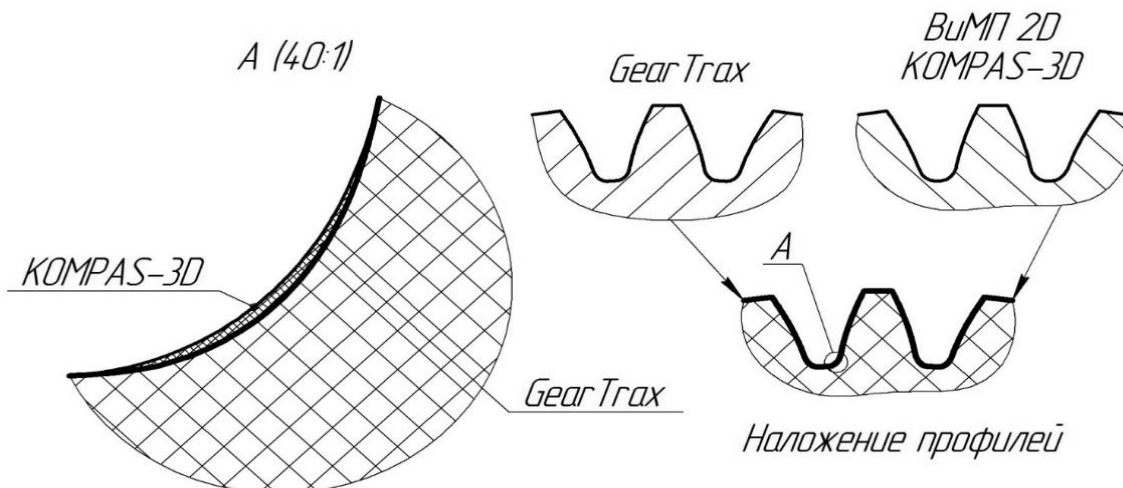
Наложение зубчатых профилей, построенных при помощи GearTrax и приложения «Валы и механические передачи 2D»
